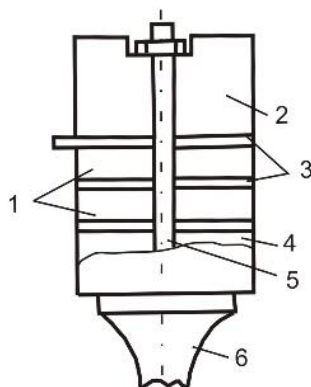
Пакетный пьезокерамический преобразователь с пассивными накладками: 1 – пьезокерамические пластины; 2 и 4 – отражающая и излучающая накладки; 3 – токоподвод; 5 – стягивающий болт; 6 – волновод-инструмент.
